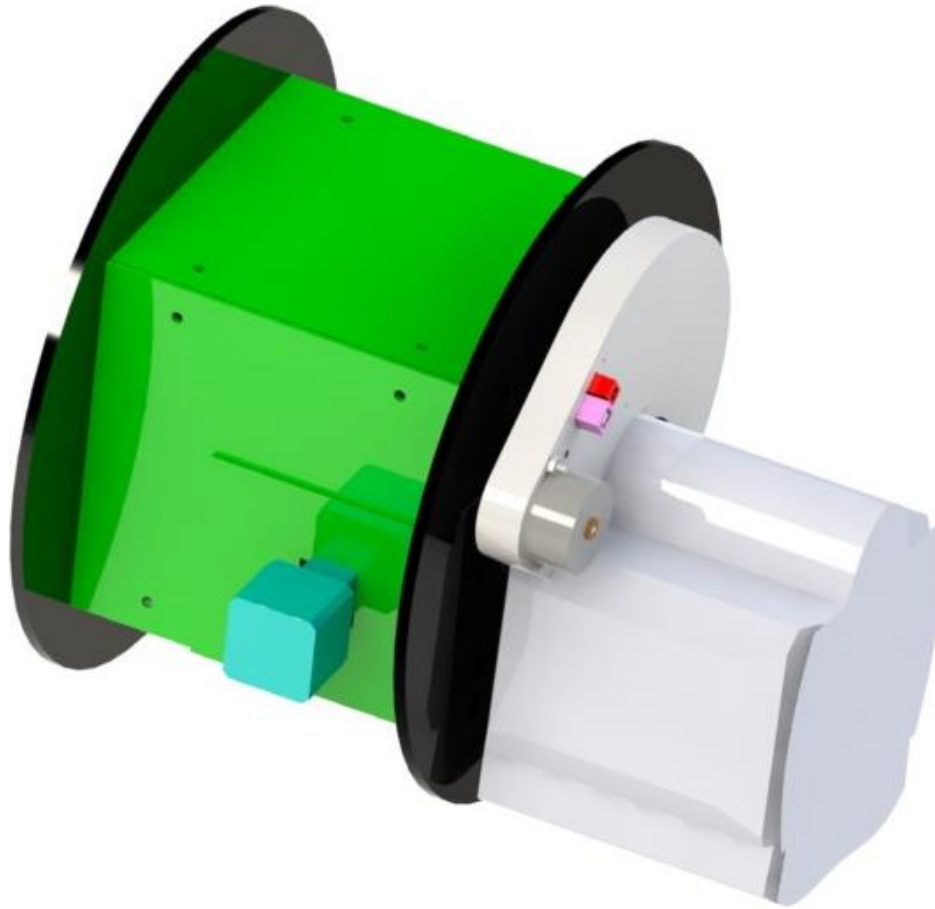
El instrumento Berkut con cubiertas de acrílico.
